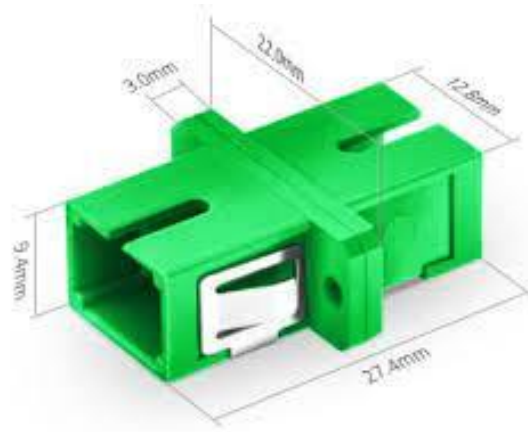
Dimensiones de un adaptador óptico. Fuente: [8].
